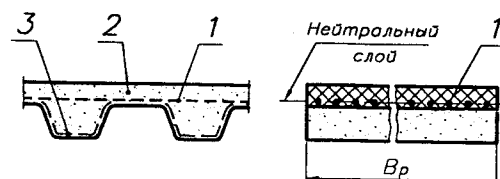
Конструкция зубчатого ремня с трапецидальными зубьями: 1 - кордшнур (металлокорд или углеродное волокно); 2 - тело ремня (маслостойкая резина, пластмасса); 3 - тканевая обкладка (для ремней, изготавливаемых методом прессования)
